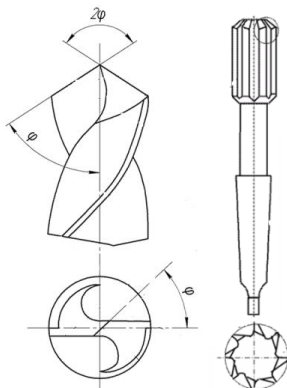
Схема сверла и развертки: а – сверло, б - развертка
